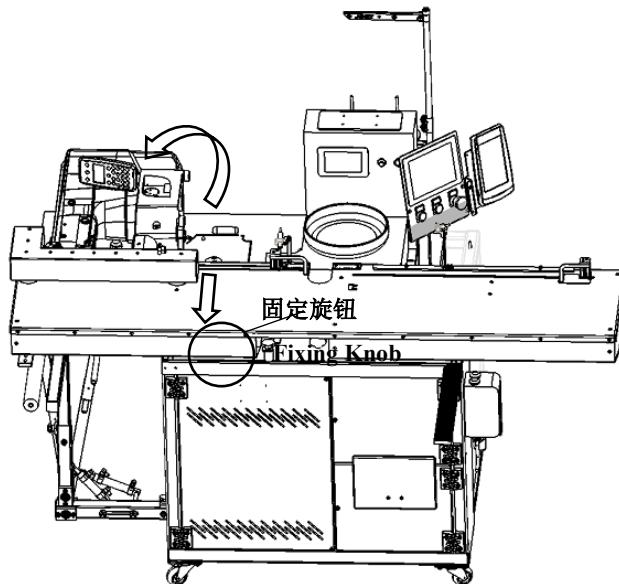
机头维修翻转图 Figure 8.4 Head repairing reverse drawing
